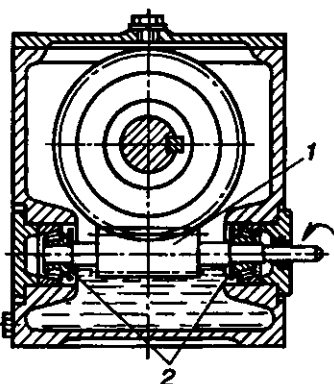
Смазка подшипников качения червячного редуктора: 1 – червяк; 2 – защитные шайбы
